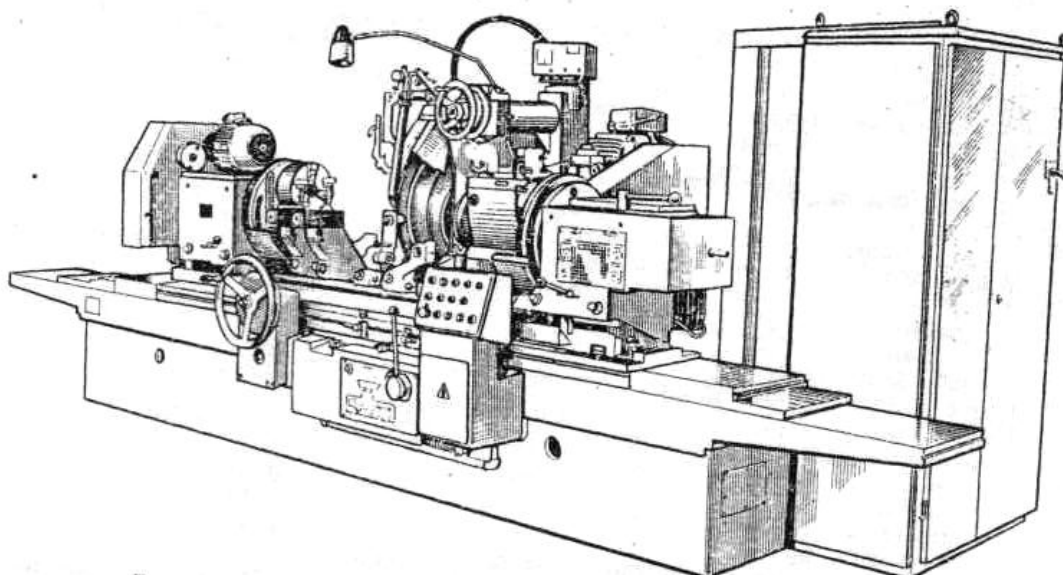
Спеціалізований колошліфувальний верстат 3Д4230 для перешліфовування шийок колінчастих валів
